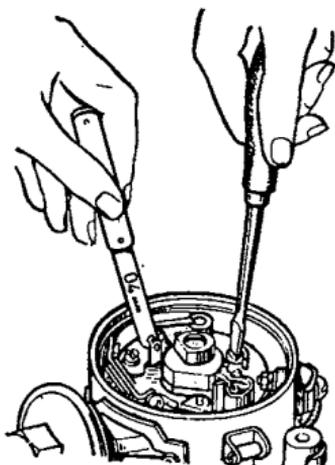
Проверка и регулировка зазора между контактами прерывателя
